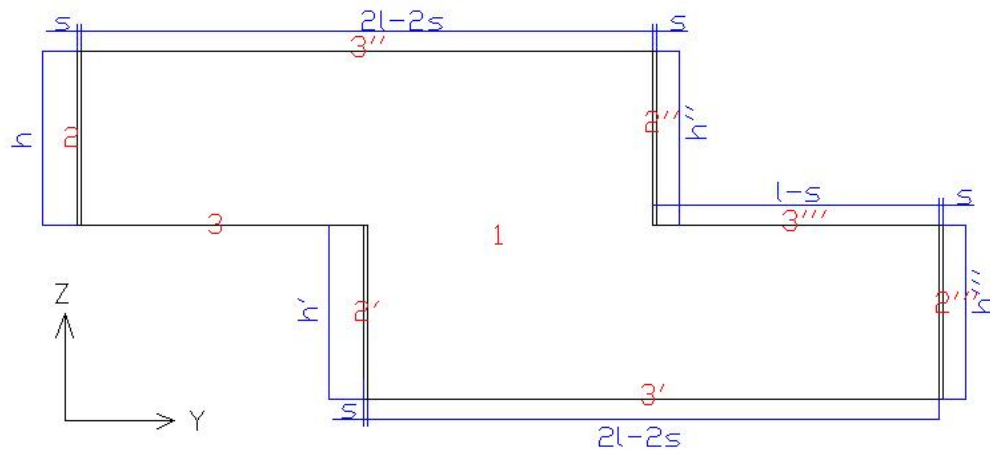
40 Vista nel piano ZY dell'assemblaggio dei pannelli
